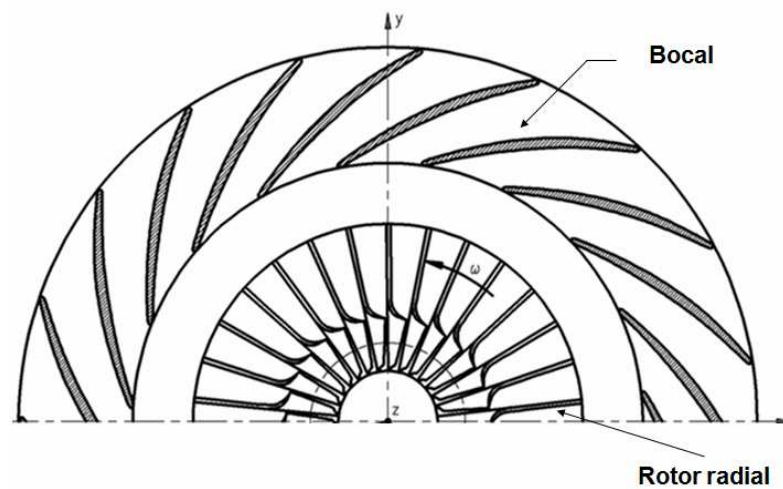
Geometria básica do bocal e rotor radial: vista frontal.
